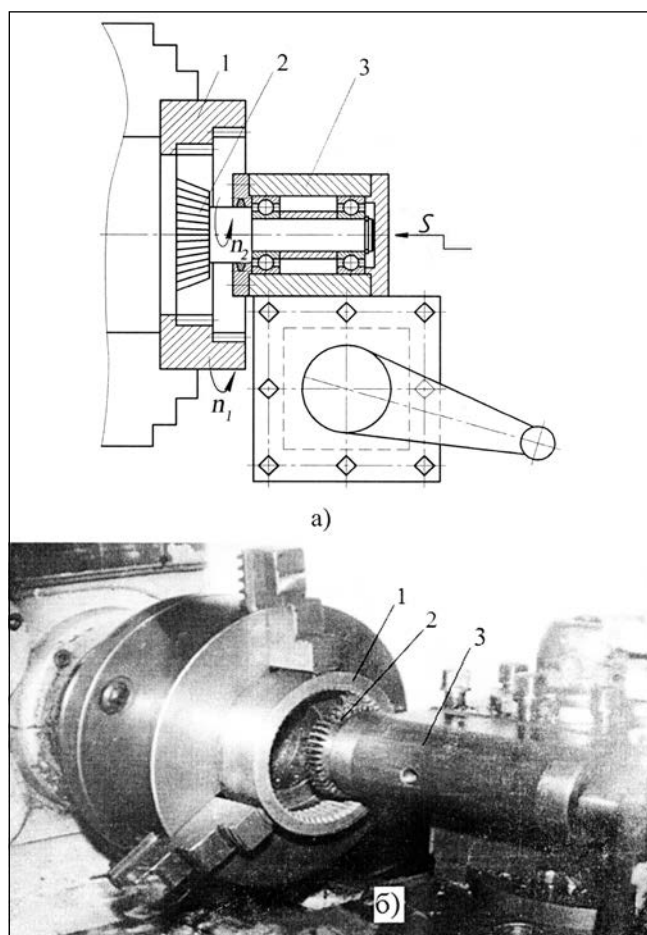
Зуботочение внутренних зубьев двухвенцового колеса: а) схема, б) рабочая зона токарного станка
